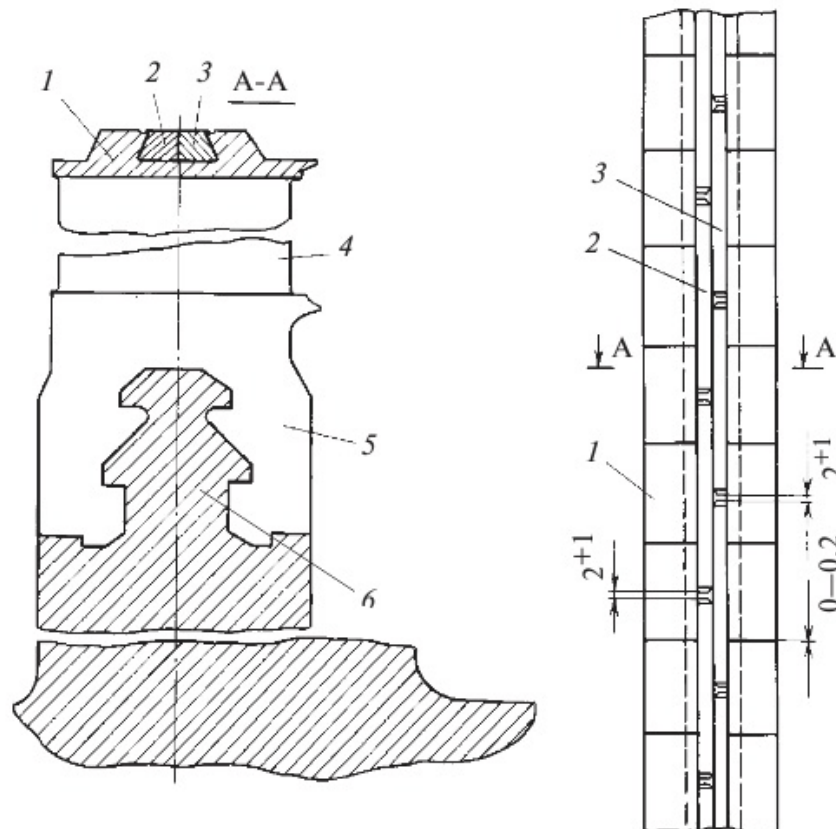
Конструкция облопачивания первой ступени цилиндра высокого давления: 1 – бандаж; 2,3 – вставки демпферные; 4 – лопатка рабочая; 5 – хвостовик; 6 – гребень диска
